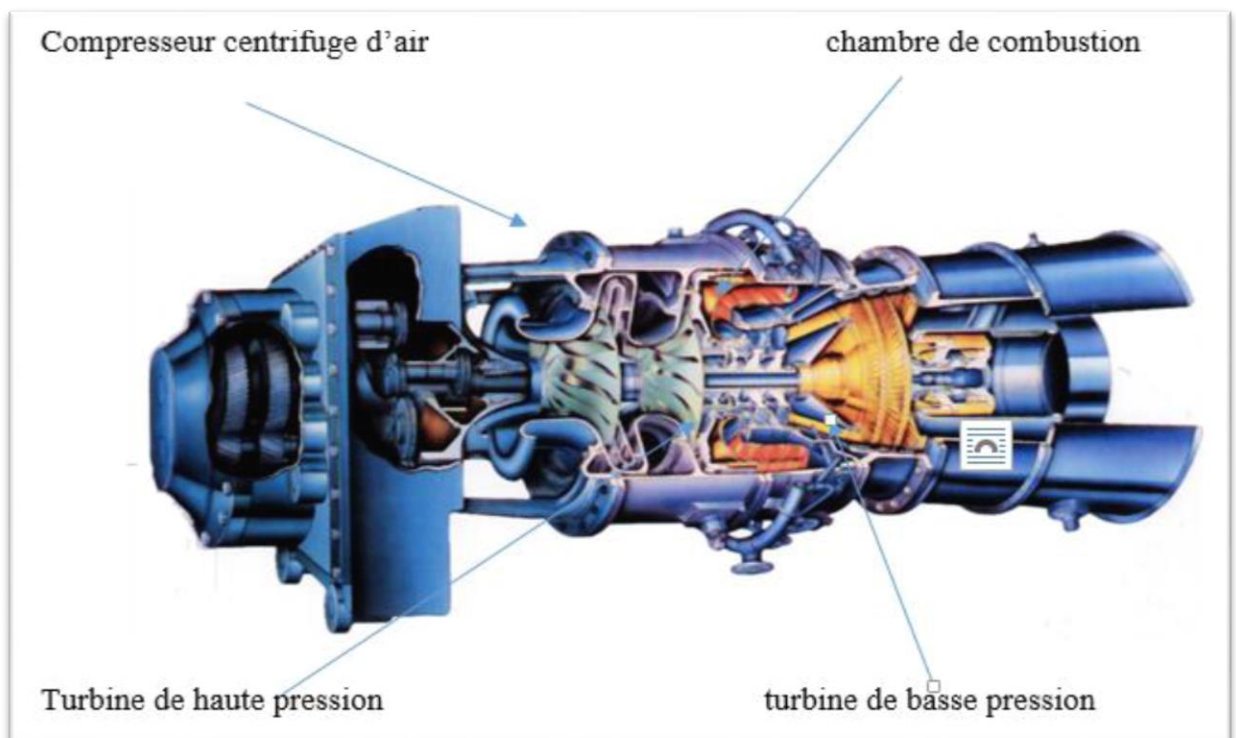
Vue d'ensemble de turbine à gaz DR 990. [1]
